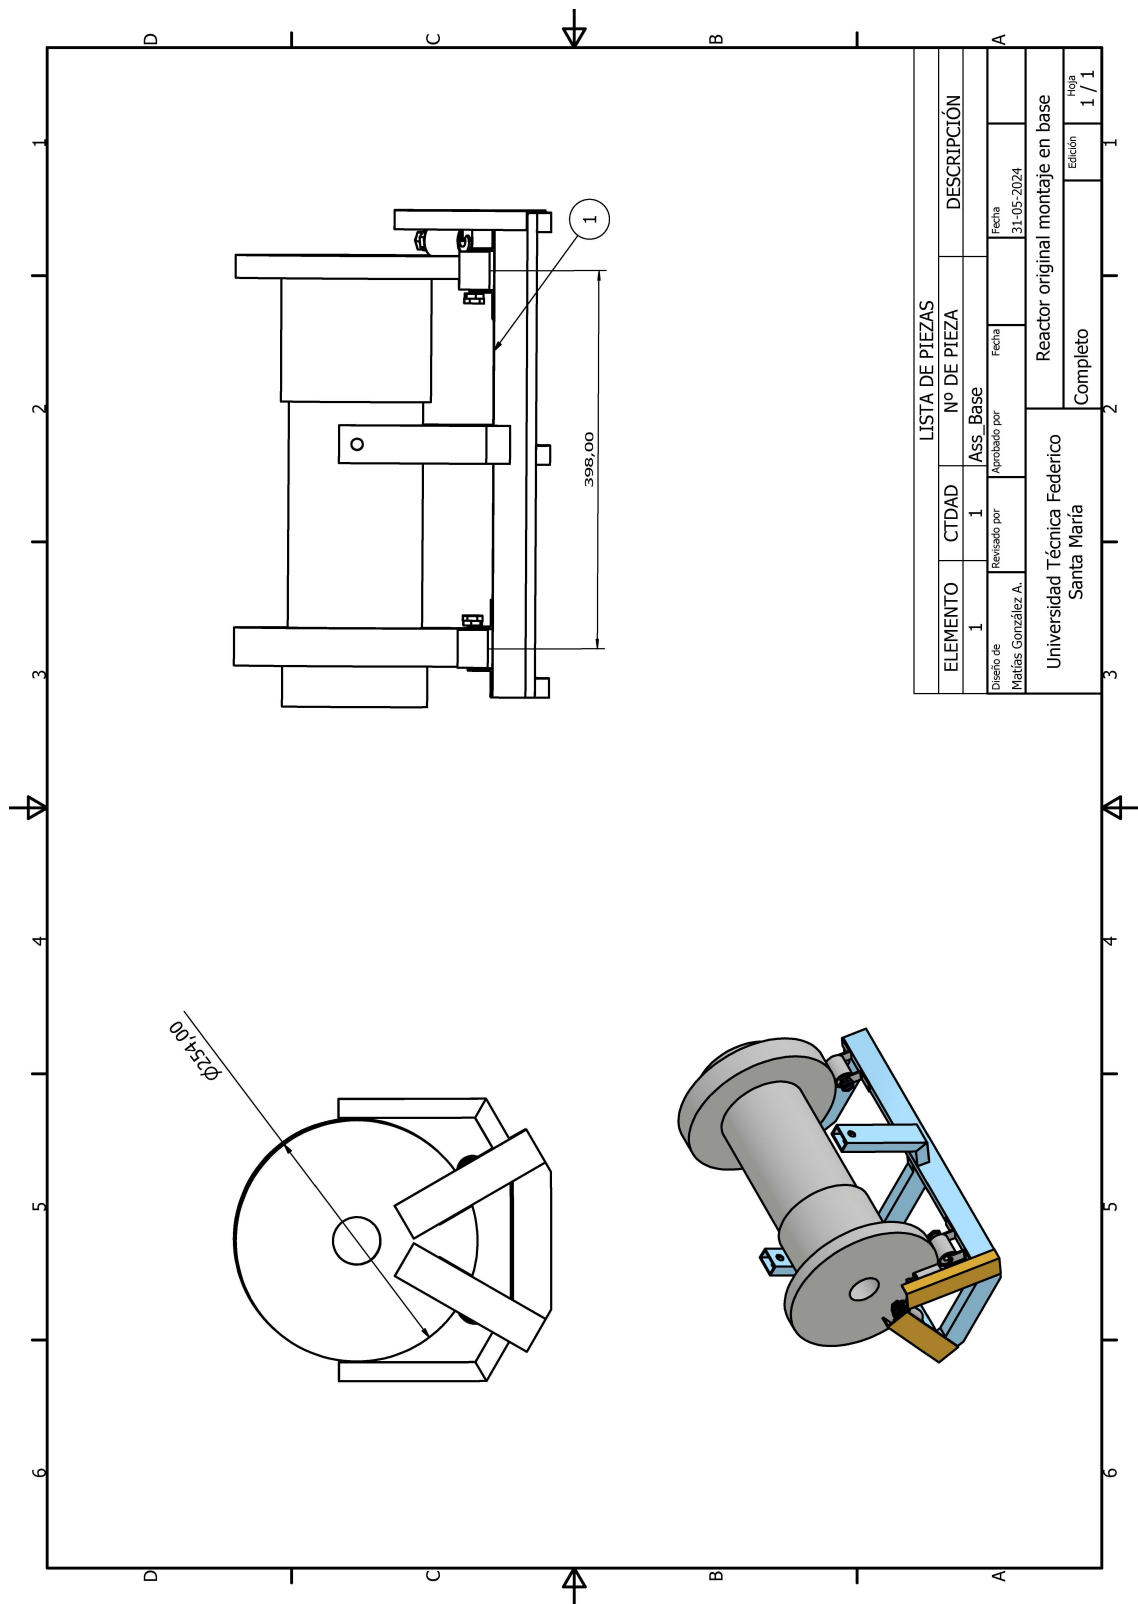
Plano del diseño original del reactor montado en base de rodamientos.
